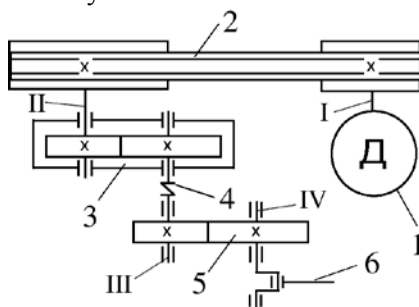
Кінематична схема привода: 1 – двигун, 2 – клинопасова передача, 3 – редуктор, 4 – муфта, 5 – відкрита зубчаста передача, 6 – кривошип O_1A ; I – IV – номери валів.
